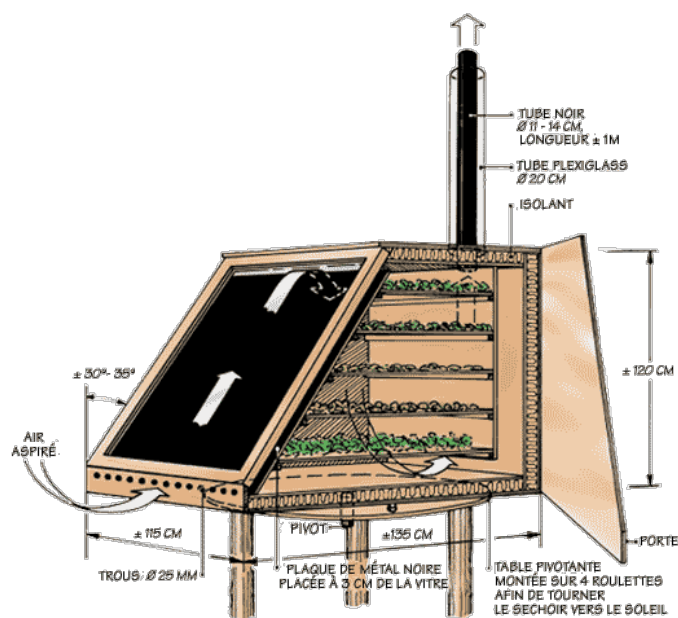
Plan d'un séchoir solaire (Onpeutlefaire.com)
